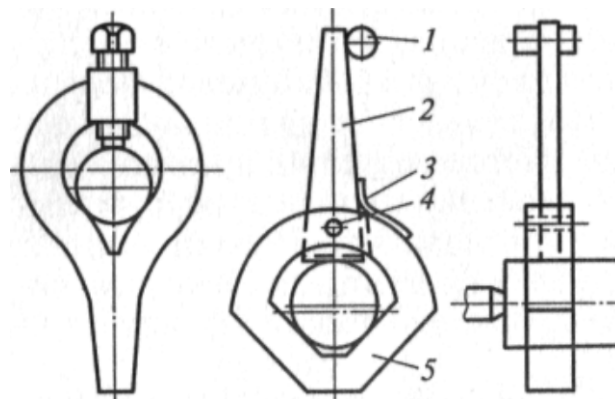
Звичайний (а) та самозатягувальний (б) токарні хомутики:
